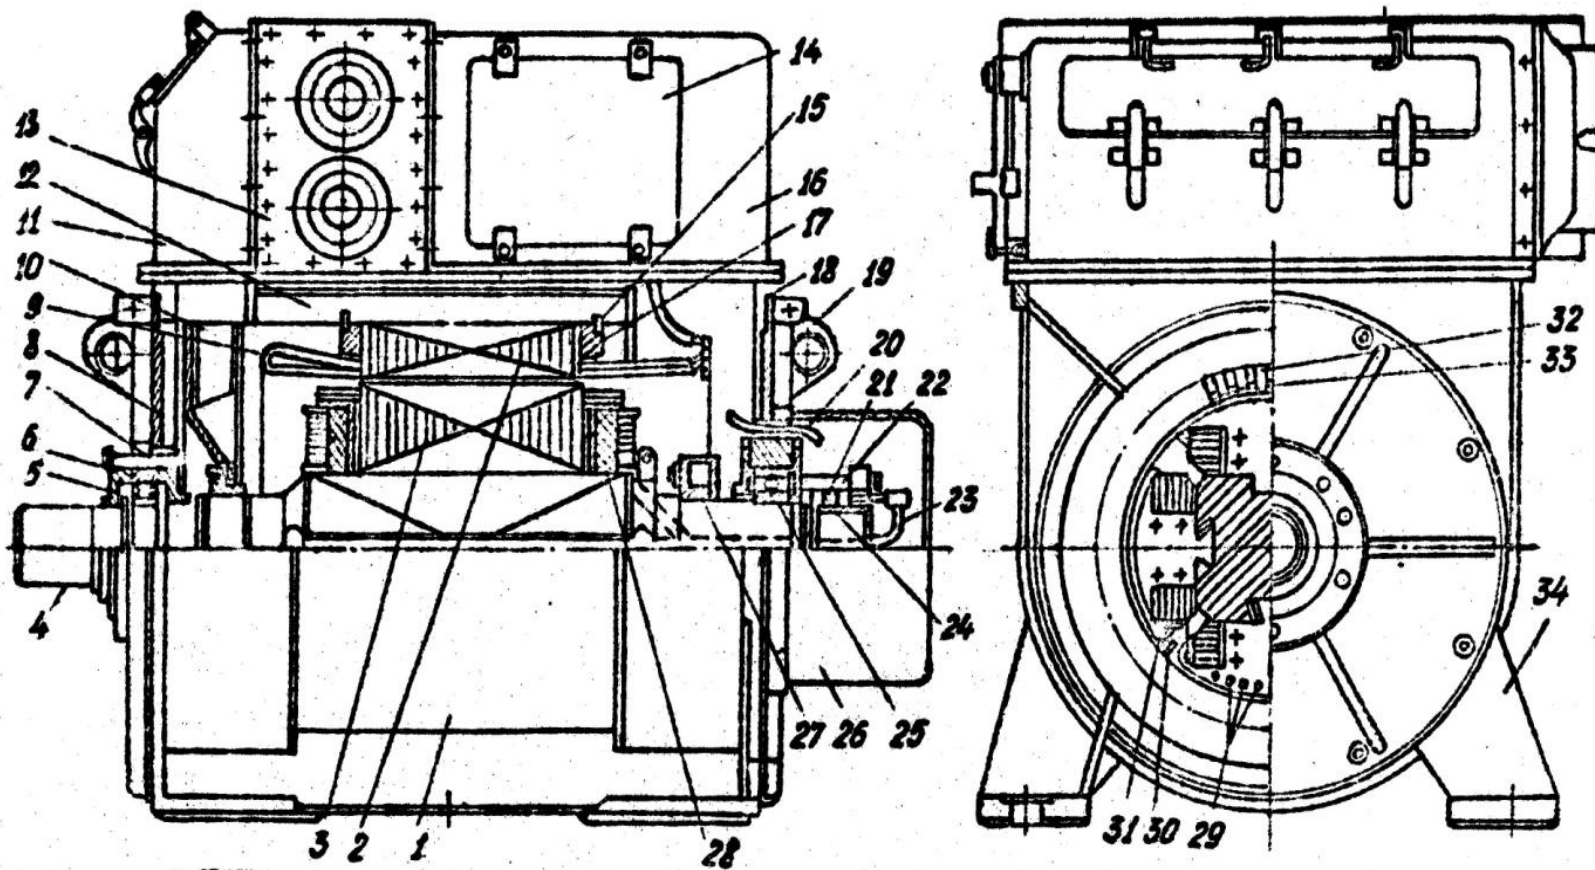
Устройство синхронного генератора серии МСК: 1 - станина; 2,3 - сердечник статора и полса рстора; 4 - вал; 5,7 - наружная и внутренняя крышки подшипника; 6,25 - роликовый и шариковый подшипники; 8,18 - задний и передний подшипниковые щиты; 9 - лобовые части обмотки статора; 10 - вентилятор; 11,16,26 - колпаки; 12 - опорные ребра; 13 - воздухоохладитель; 14 - люки; 15 - шпонка; 17 - щеки; 19 - рым; 20 - кабель для соединения обмотки возбуждения с силовой системой возбуждения; 21 - контактные кольца; 22 - щеточное устройство; 23 - выводные концы обмотки возбуждения; 24 - втулка; 27 - балансировочная втулка; 28 - изоляция; 29 - демпферная обмотка; 30 - соединительные болты; 31 - катушка обмотки возбуждения; 32 - паз; 33 - клин; 34 - лапы
